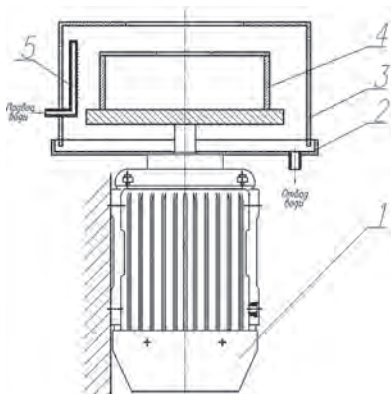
Схема экспериментальной установки центробежного литья с вертикальной осью вращения: 1 – электродвигатель; 2 – лоток для отвода охладителя; 3 – защитный кожух; 4 – форма для центробежного литья; 5 – охлаждающая форсунка
